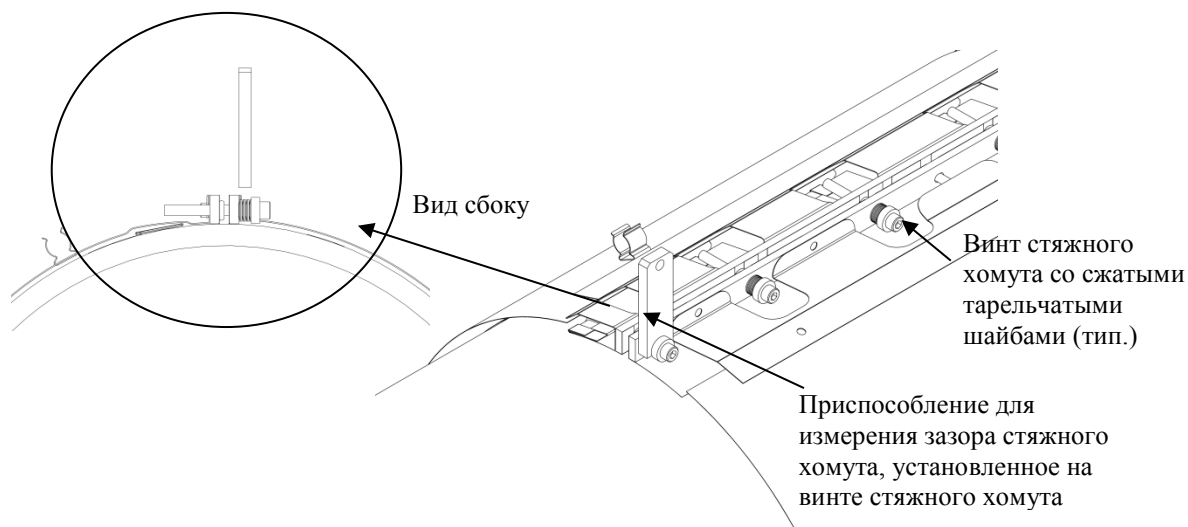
Приспособление для измерения зазора стяжного хомута, установленное на винте стяжного хомута
